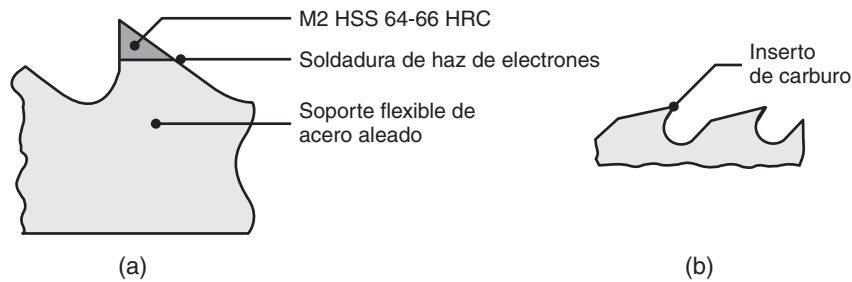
(a) Dientes de acero de alta velocidad soldados en una hoja de acero. (b) Insertos de carburo unidos por soldadura fuerte a los dientes de la hoja.
